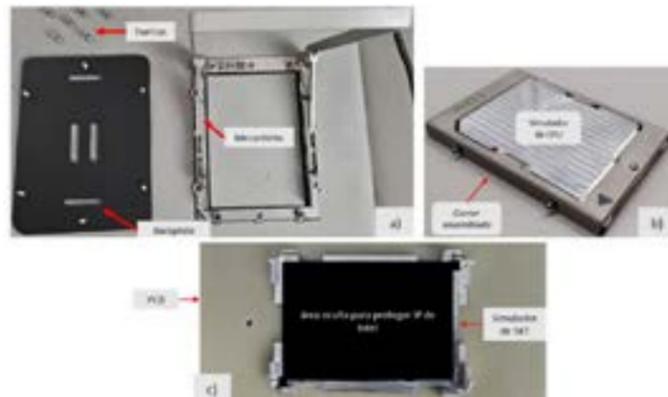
a) Placa trasera, mecanismo; b) carrier y simulador de CPU y c) PCB y SKT.
